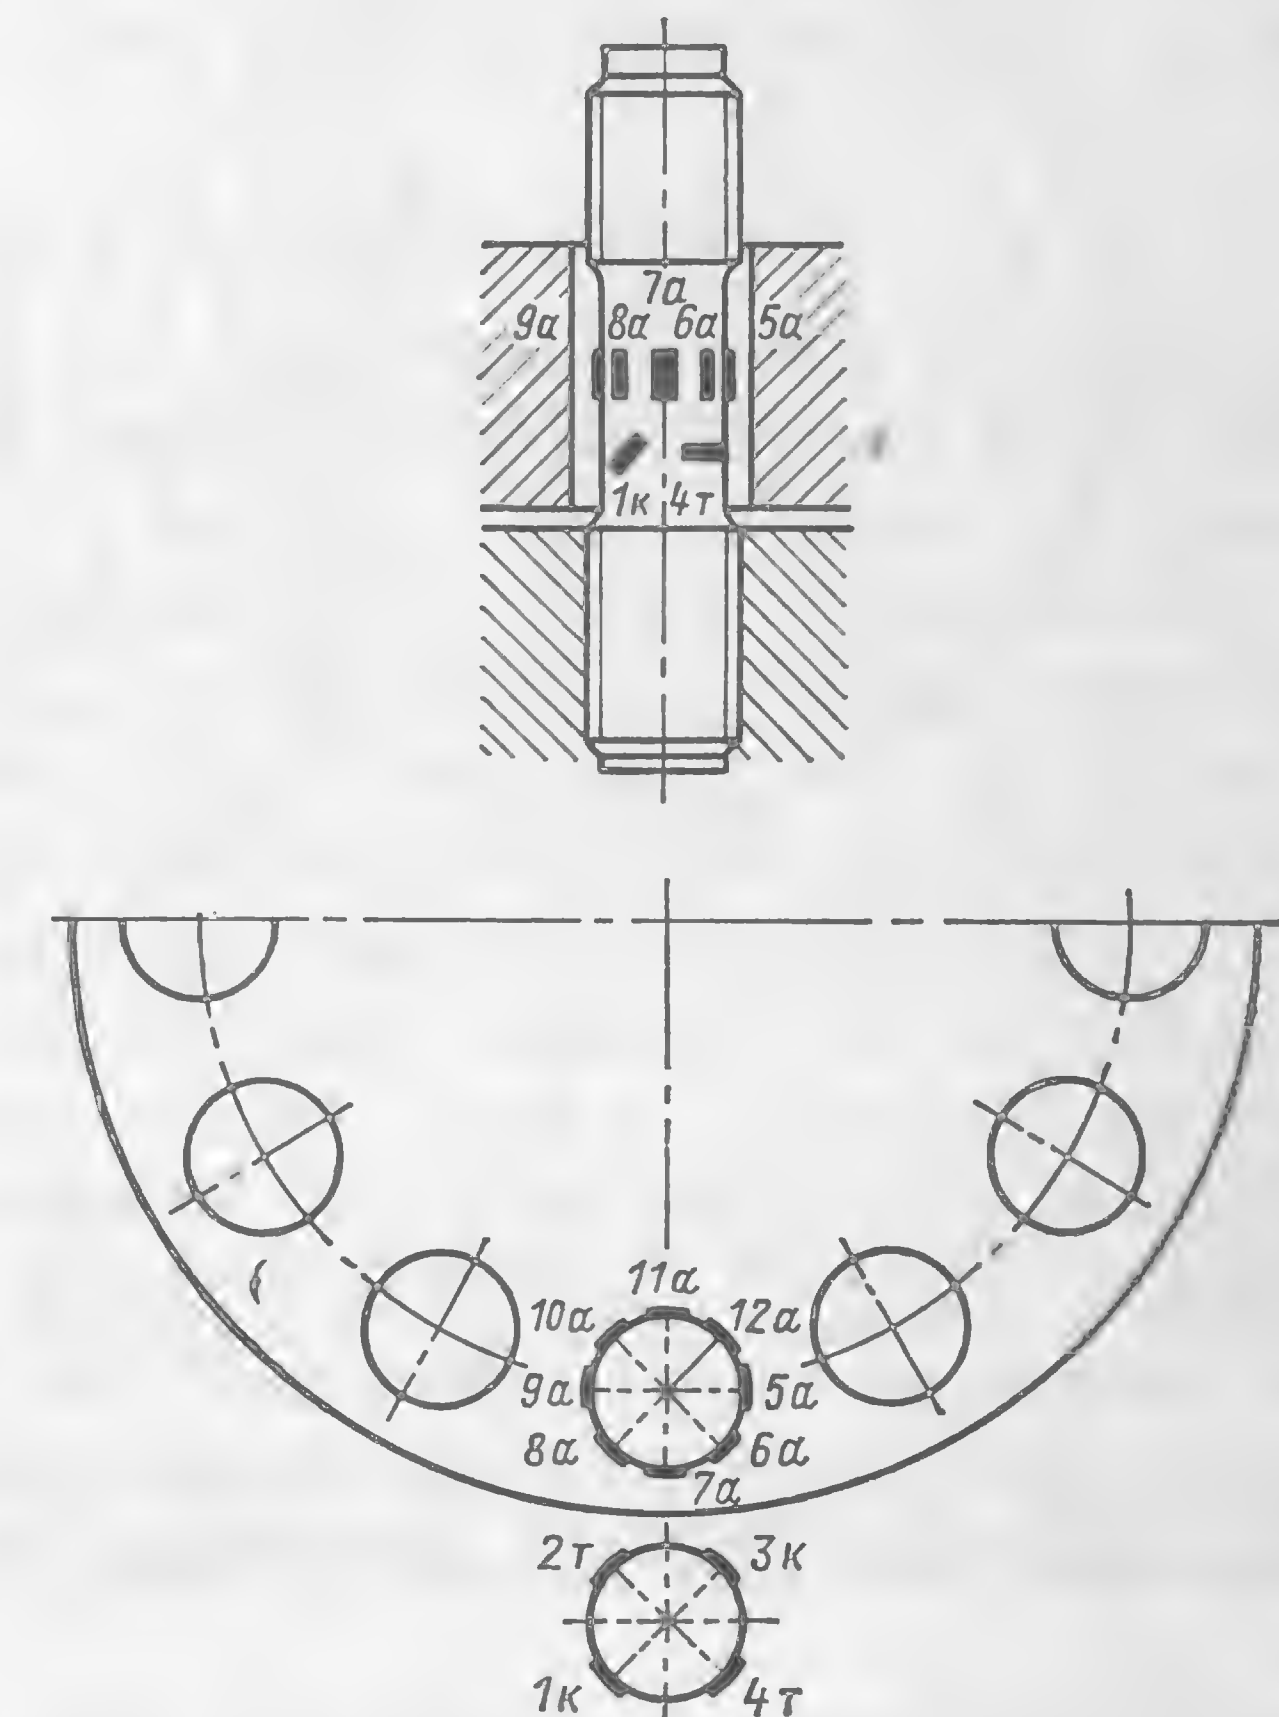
Установка проволочных тензодатчиков на шпильке для контроля напряжений при затяжке.
